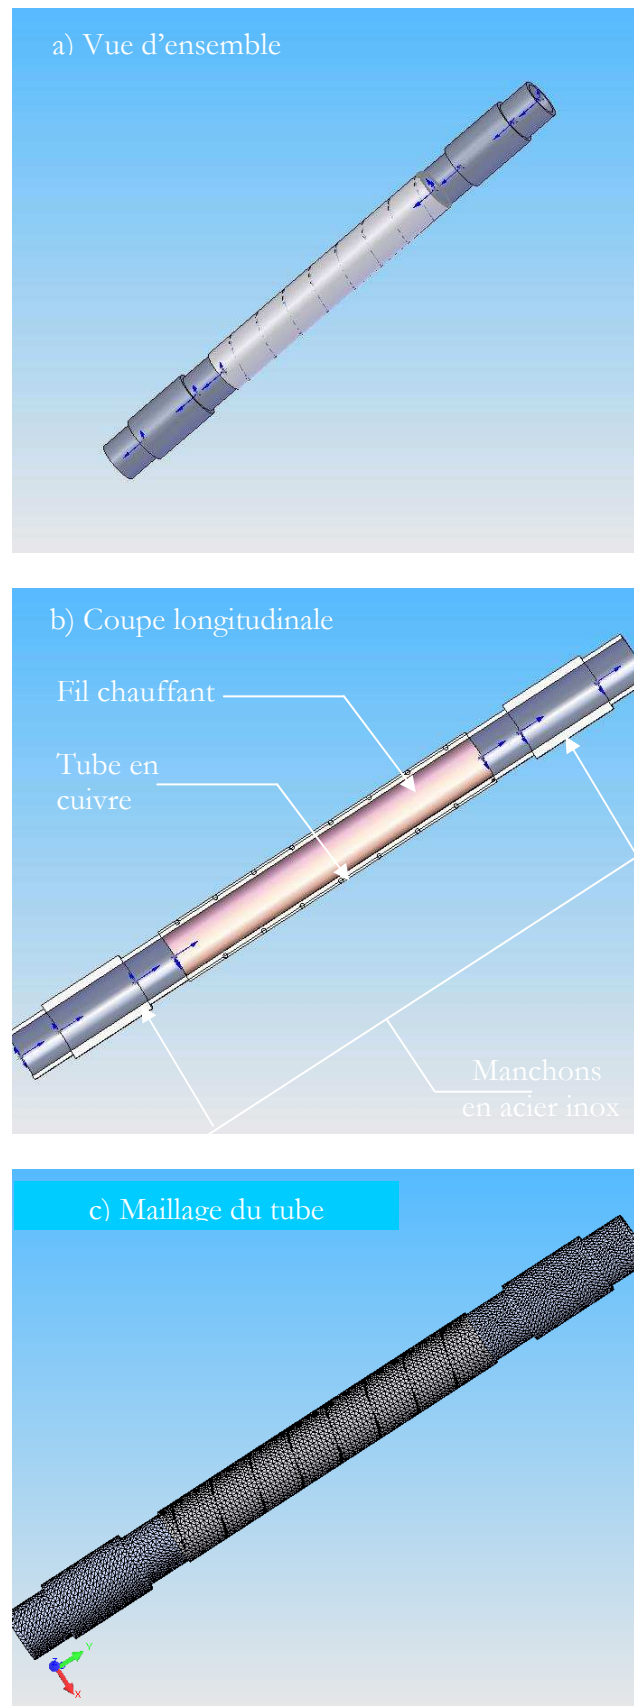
a) Vue d'ensemble de la section d'essai b) Coupe longitudinale de la section d'essai c) Maillage de la section d'essai.
